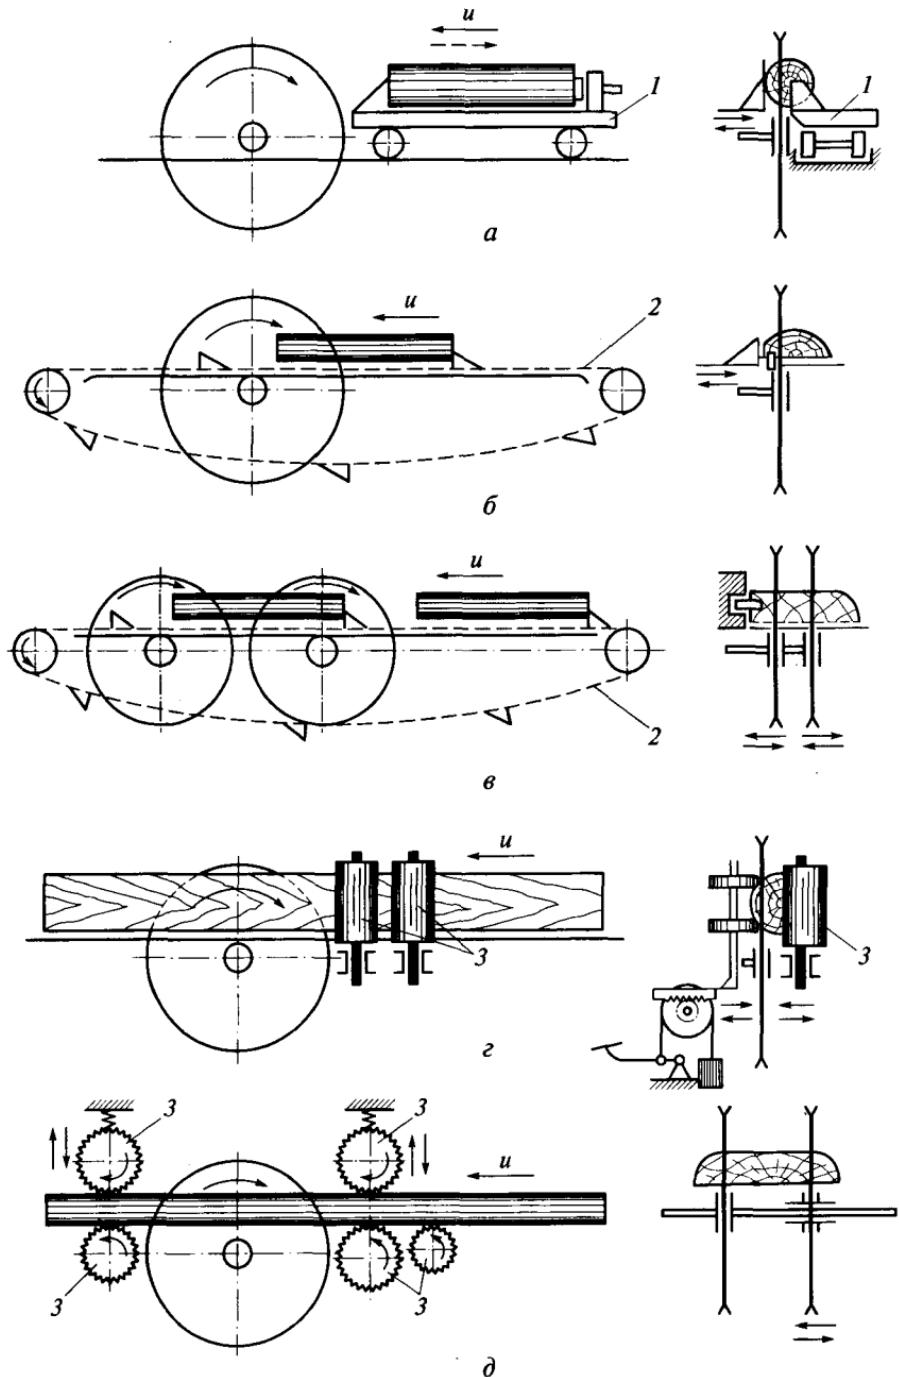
Схемы круглопильных станков для продольной распиловки:
